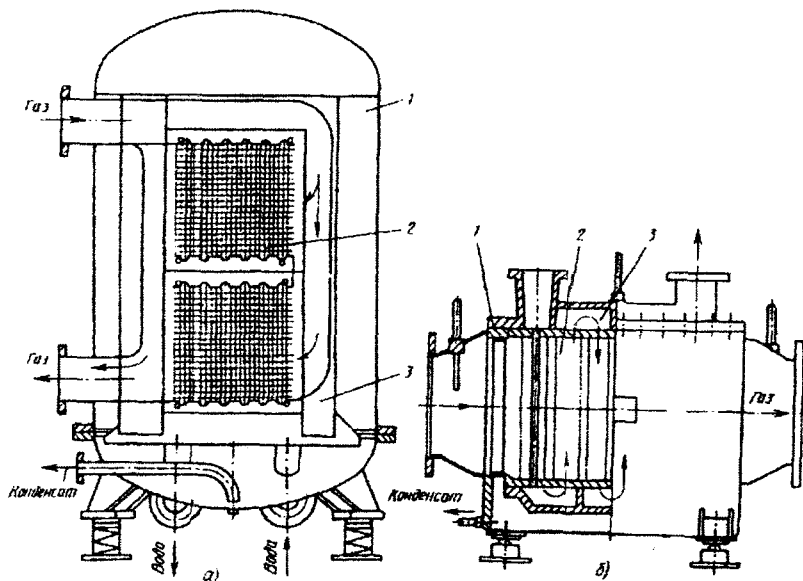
Промежуточный (а) и концевой (б) охладители турбокомпрессоров:
